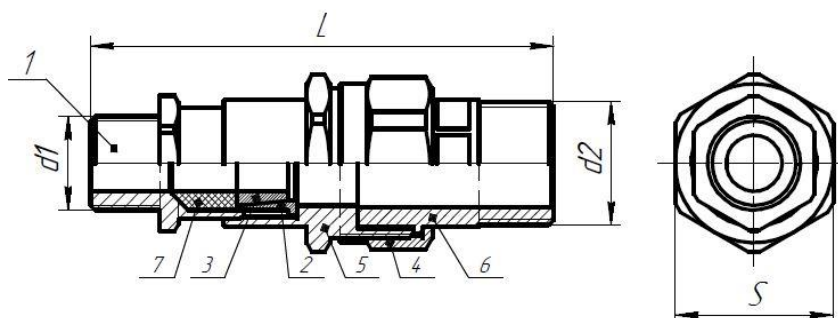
Общий вид кабельного ввода ВА с фитингом для крепления трубы.
